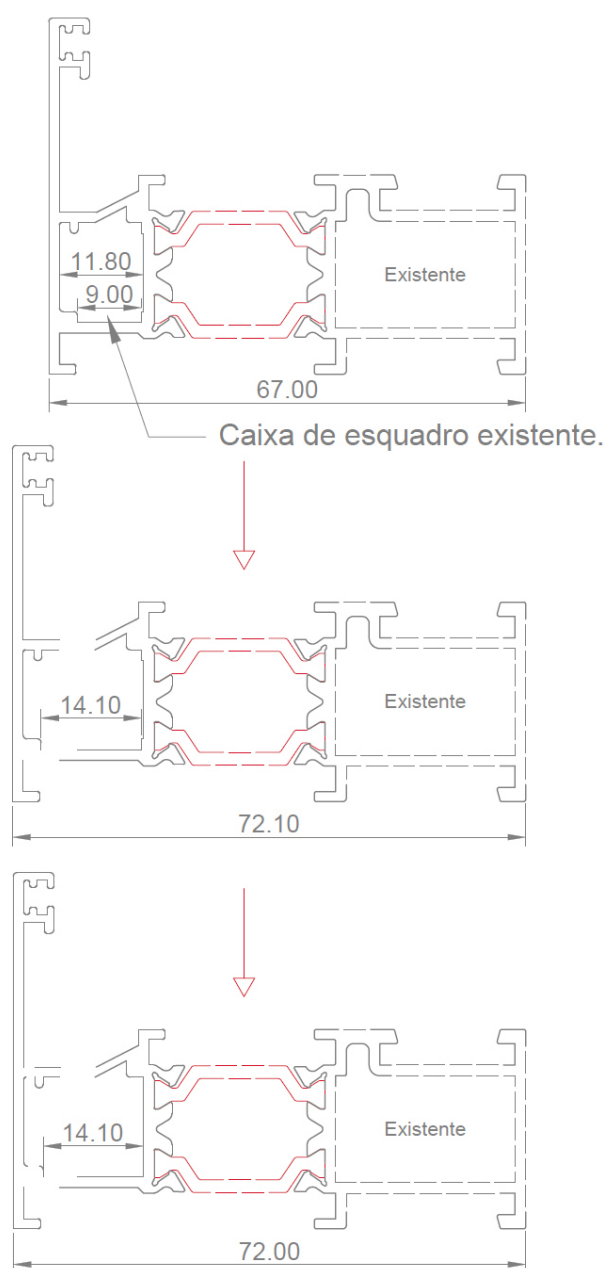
Aumento da largura do aro fixo afastando a parede exterior (esquerda).
